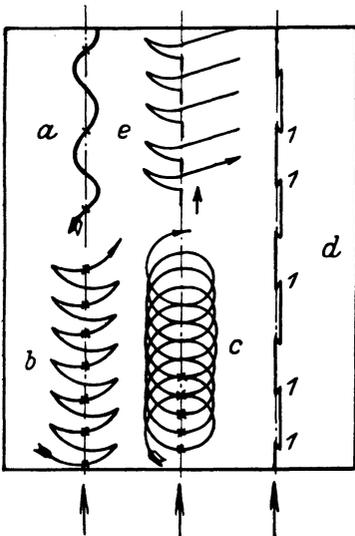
Brennerbewegung beim Schweißen.
